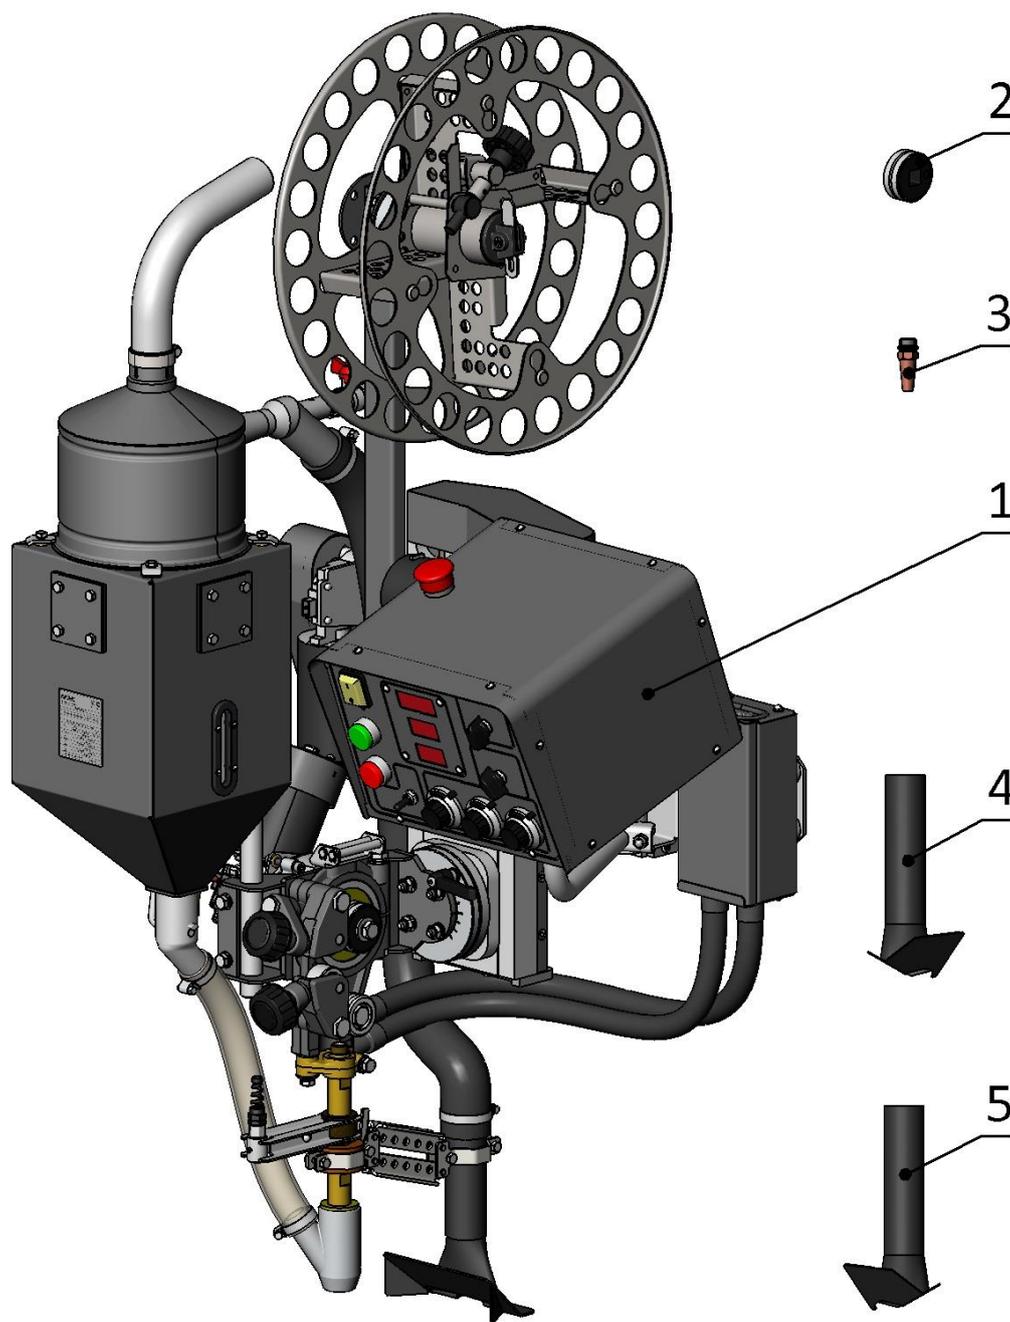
Автомат сварочный АДФ-1000 УЗ сер.06 исп.05.
